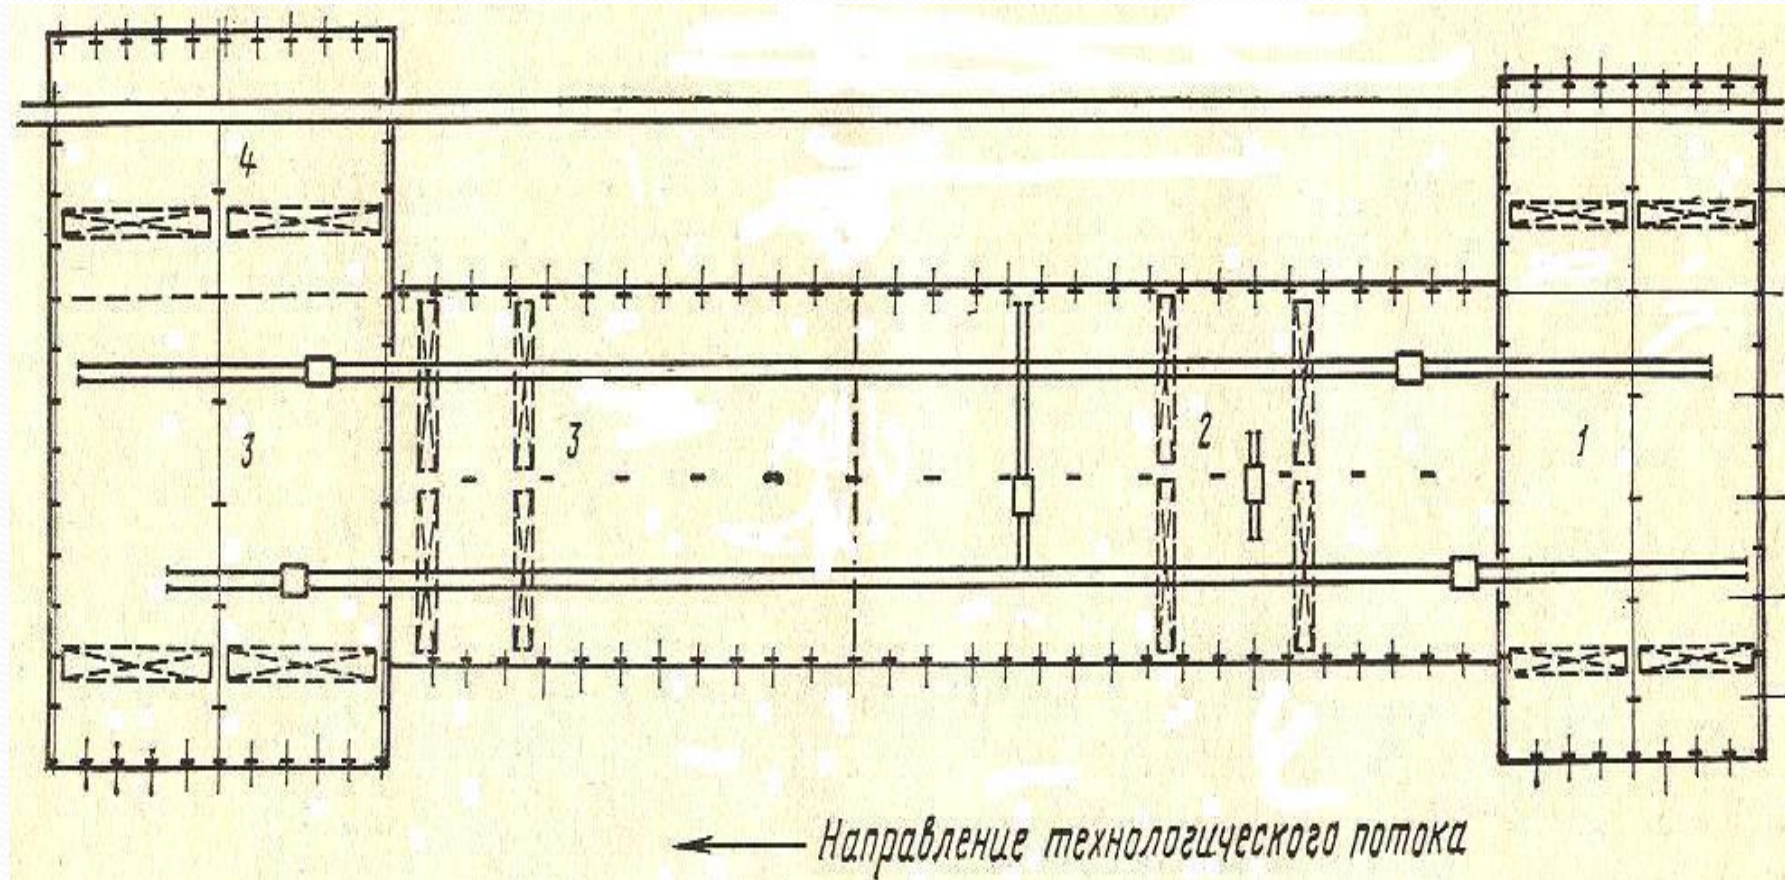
Транспортно-технологическая схема завода со смешанным расположением пролетов: 1 - цех подготовки со складом металла; 2 - цех обработки со складом полуфабриката; 3 - цех сборно-сварочный; 4 - цех малярно-погрузочный
